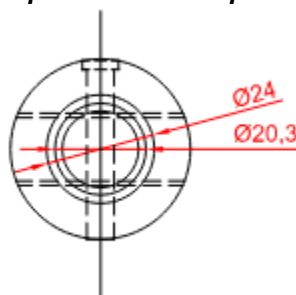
Desenho explodido em três partes do dispositivo (parte 3/3)
